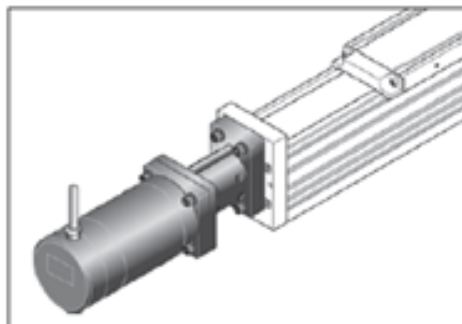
Motor de montagem com acoplamento e motor de piso [19]
